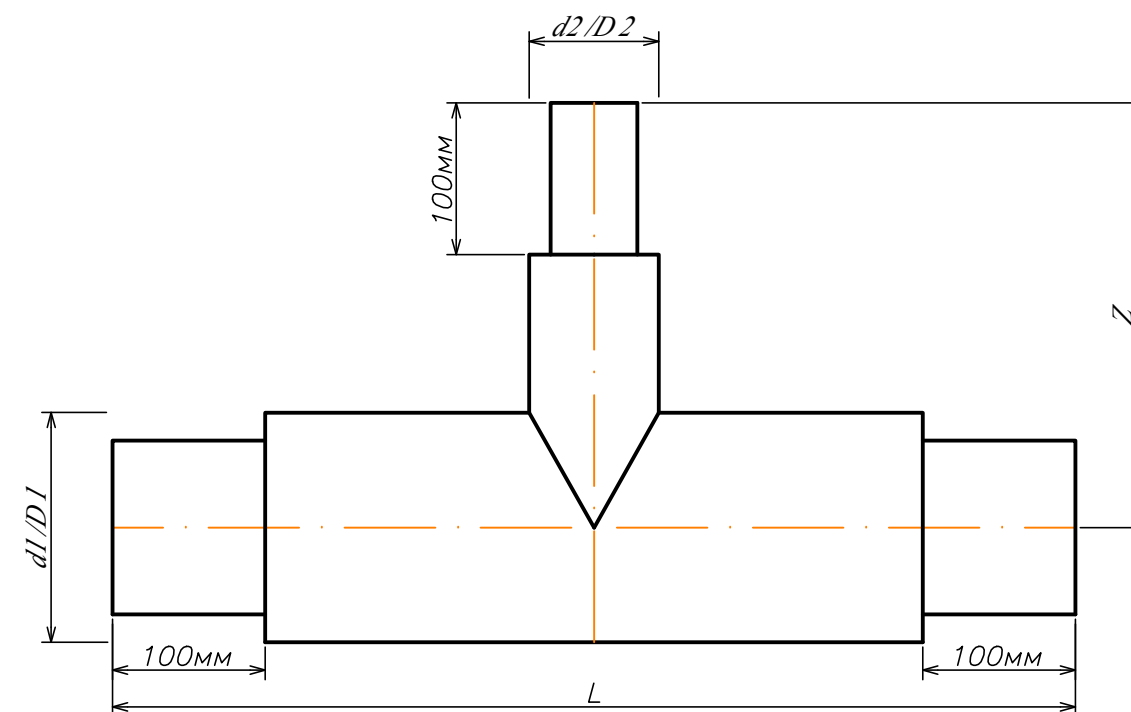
Тройник неравнопроходной сварной предизолированный
